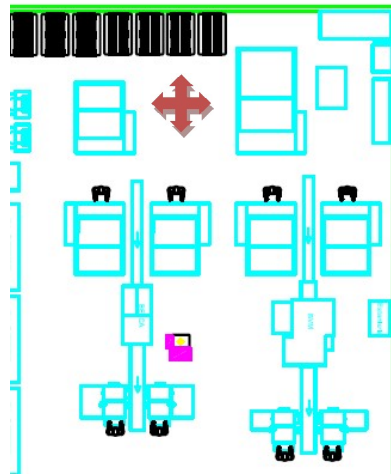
Vista en planta de la ubicación del nuevo puesto de lectura en la zona de montaje.
